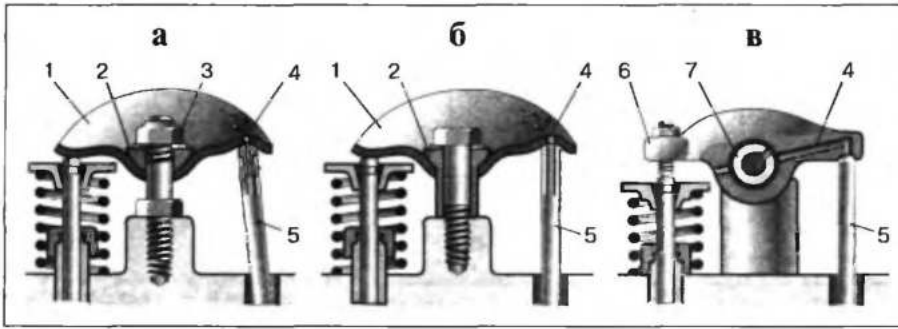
Схемы привода клапанов у двигателей с нижним распределительным валом (OHV): а — с "подвесной" опорой коромысла; б — с жесткой опорой коромысла; в — с общей осью коромысел; 1 — штампованное коромысло; 2 — опорная шайба; 3 — гайка с "тугой" резьбой; 4 — отверстие подачи масла; 5 — штанга; 6 — питое коромысло; 7 — ось коромысел
